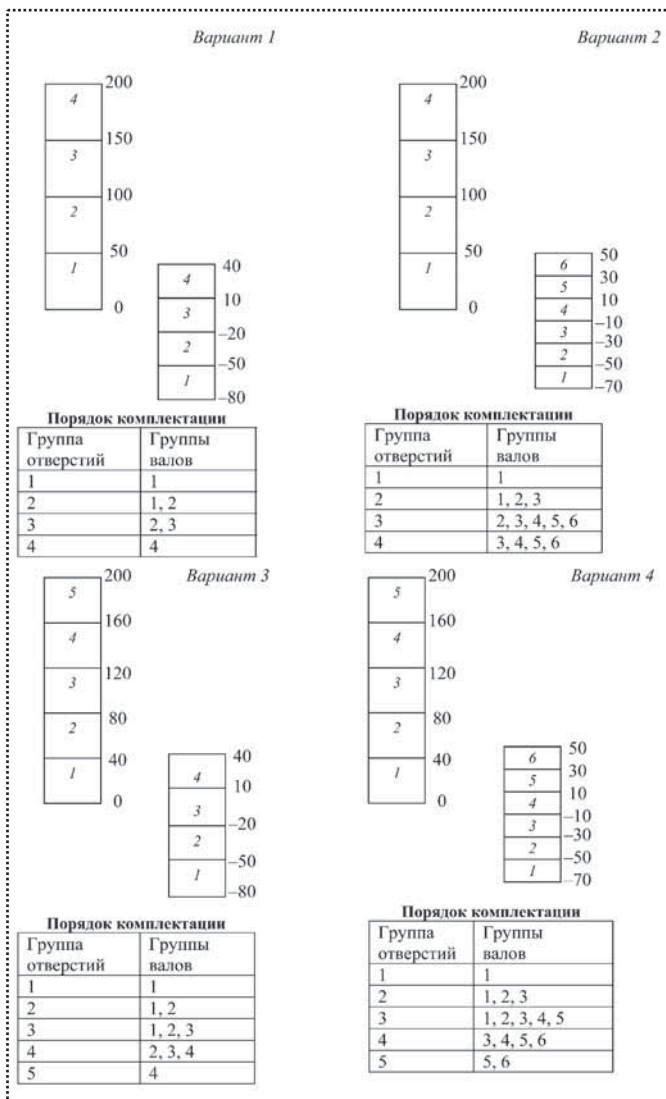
Схемы сборки и порядок комплектации отверстий валами
